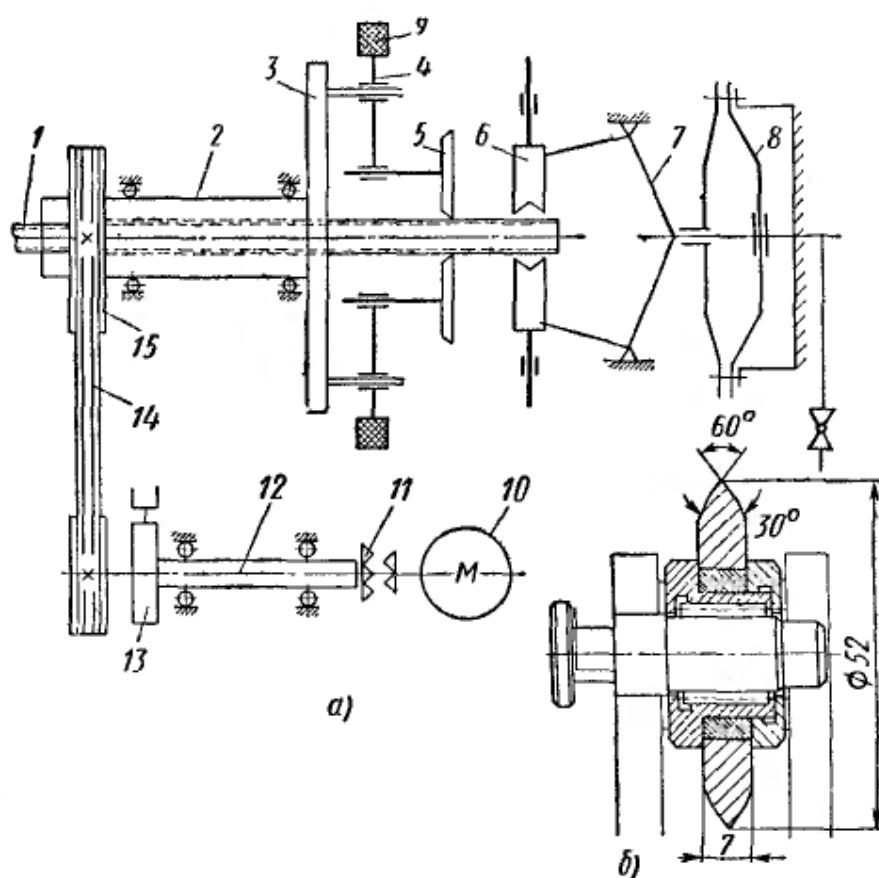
Схема станка для разрезки труб (а) и твердосплавный нож (б):
